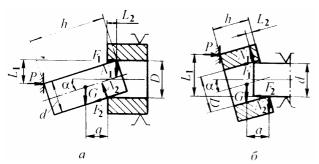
Схема горизонтальной сборки соединения: а) – установка вала во втулку,
